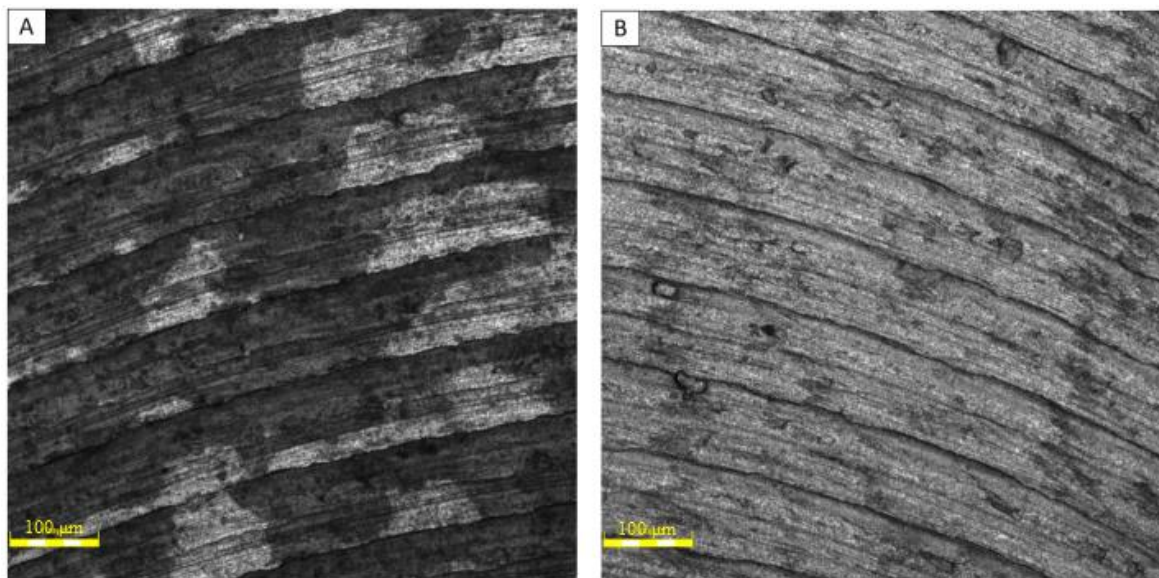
Imagens dos canais usinados: A) Canal 1 - Usinado com um bocal à 45° e com vazão de 20 l/min. e B) Canal 8 - Usinado com bocal à 45° e com vazão de 10 l/min.
